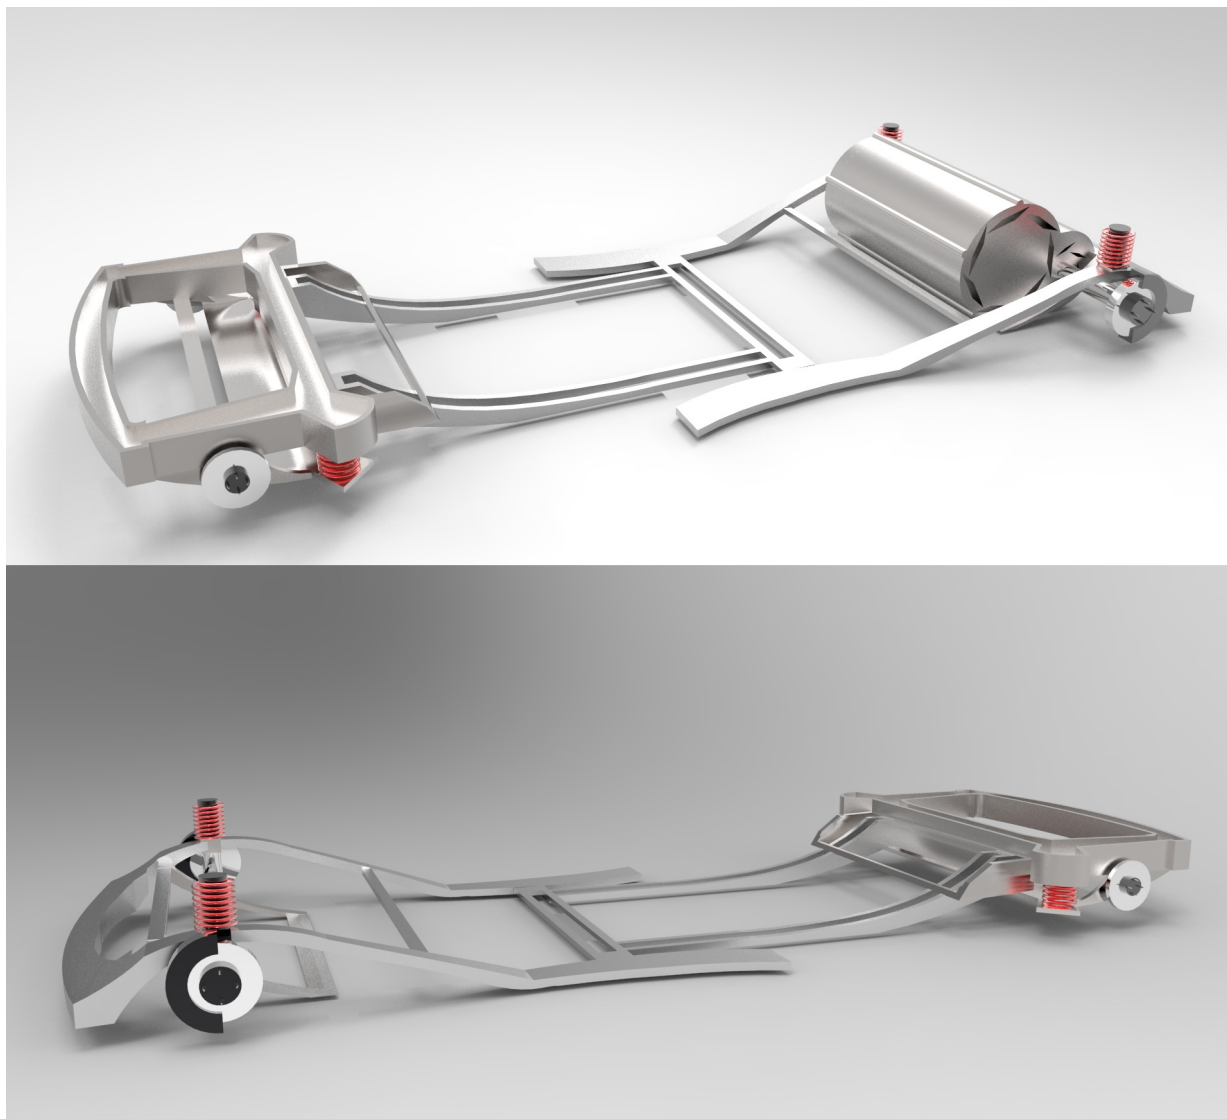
Representação da estrutura do *chassi* em alumínio fundido com e sem o motor acoplado.
